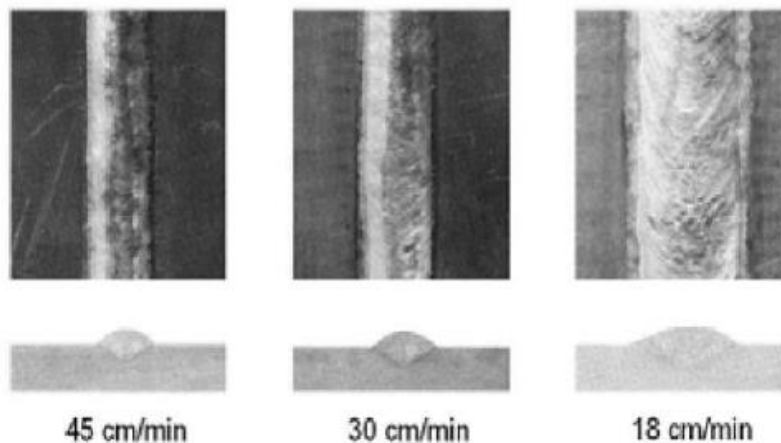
Efeito da velocidade de soldadura na penetração da solda [29].
